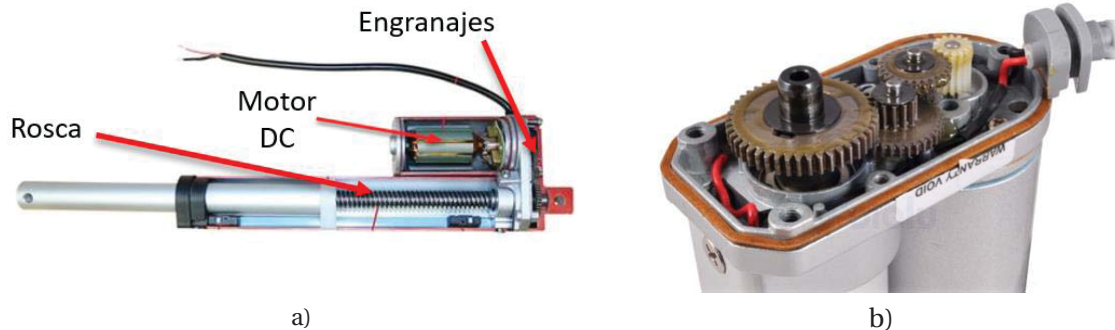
a) Principales componentes del actuador lineal, b) Juego de engranajes [65]
